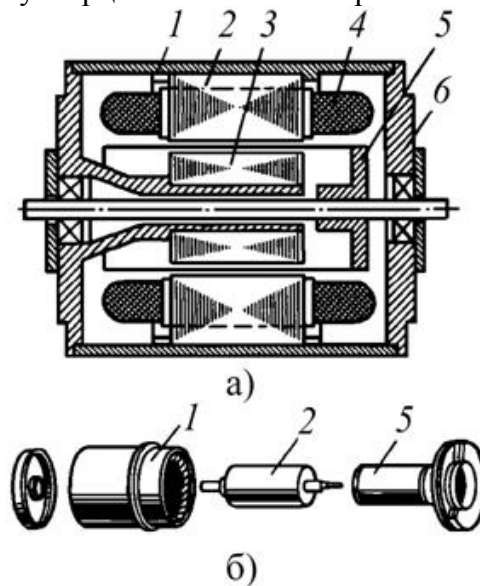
Конструкція двигуна з порожнім немагнітним ротором (а) та його основні конструктивні елементи (б): 1 - корпус; 2 - зовнішній статор; 3 - внутрішній ротор; 4 - обмотка статора; 5 - порожній немагнітний ротор; 6 - підшипниковий щит.
